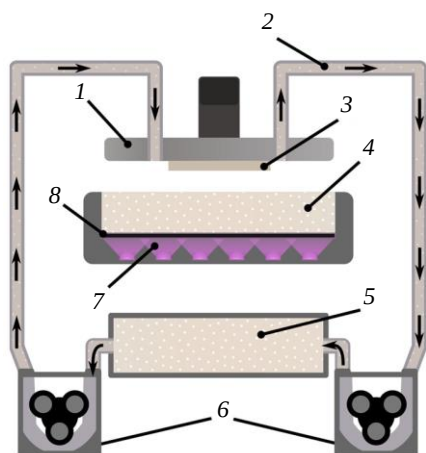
Система рециркуляции смеси для послойного фотоотверждения с помощью 3D-принтера
